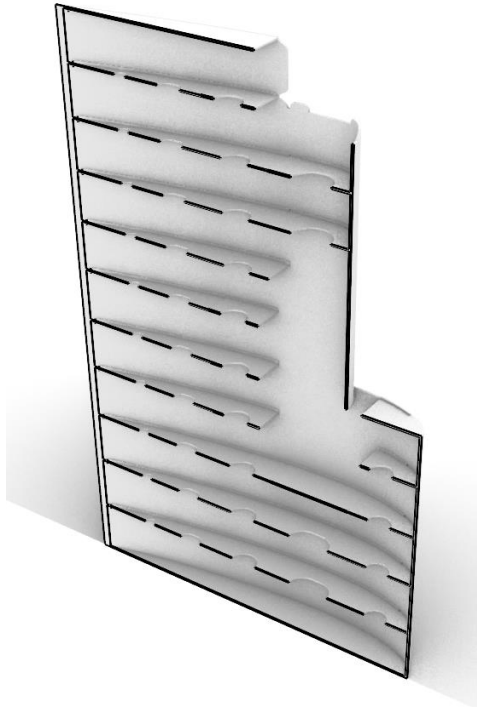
Μοντέλο *upper casting* (τρισδιάστατη απεικόνιση)
